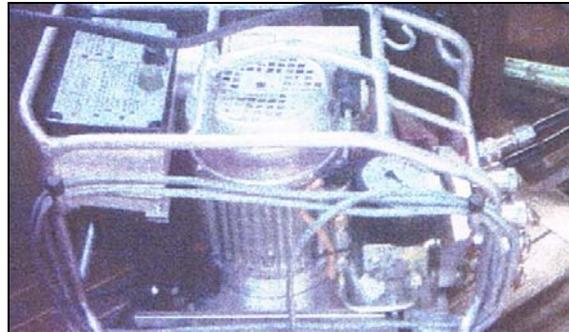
Llave dinamométrica electro-hidráulica. Fuente: autor
